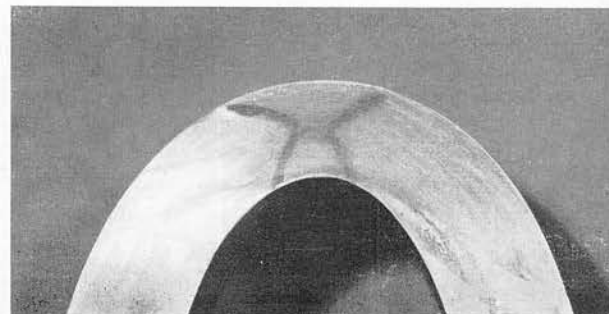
Prüfung einer Schweißnah an einer Biegeprobe
